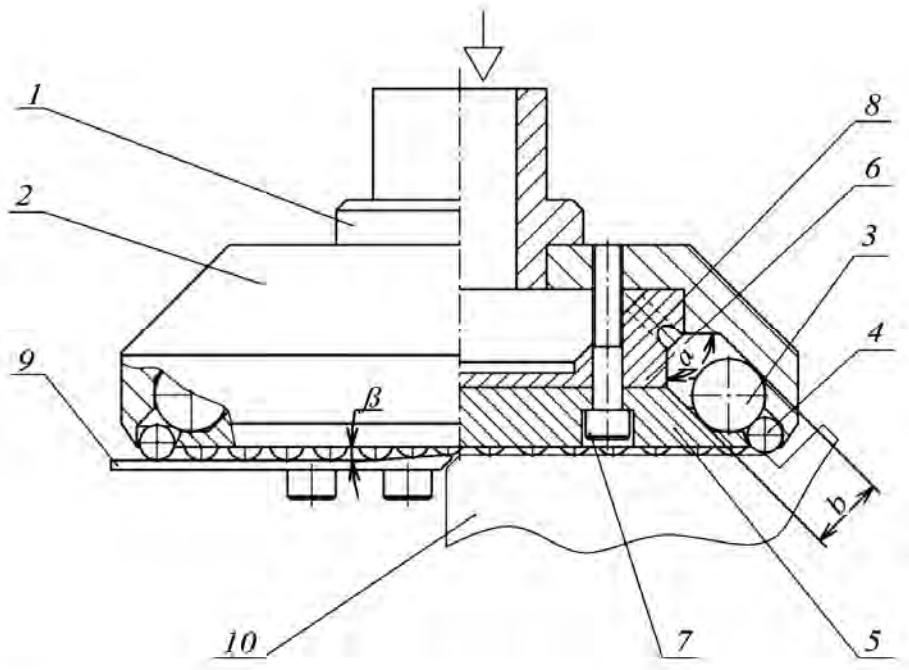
Конструктивная схема инструмента для пневмовибродинамической обработки плоских поверхностей [4]
